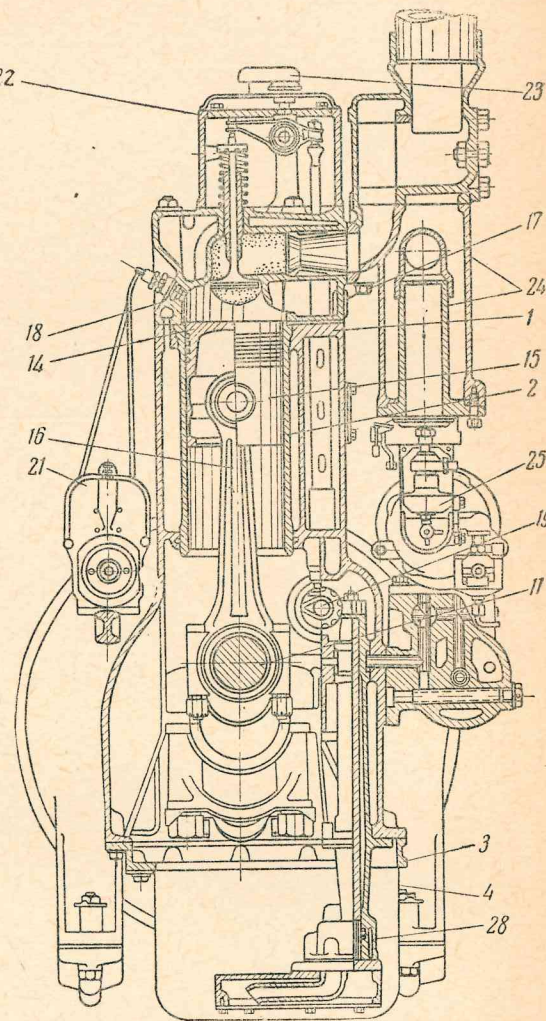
Поперечный разрез двигателя СТЗ-НАТИ
